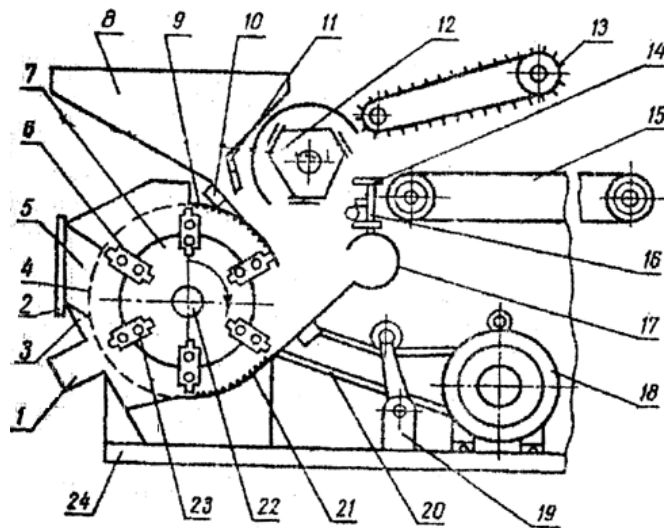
Схема дробарки КДУ-2: 1- відсосуючий патрубок; 2- кришка вивантажувального люка; 3- вставна викидна горловина; 4- решето; 5- кришка дробильної камери; 6- молоток; 7- диск ротора; 8- бункер; 9- верхня дека; 10- верхній магнітний сепаратор; 11- поворотна заслінка; 12- ріжучий барабан; 13- пресуючий транспортер; 17- підвідний повітряний патрубок; 18- електродвигун; 19- натяжний пристрій; 20- нижній магнітний сепаратор; 21- нижня дека; 22- вал ротора; 23- вісь; 24- рама.
